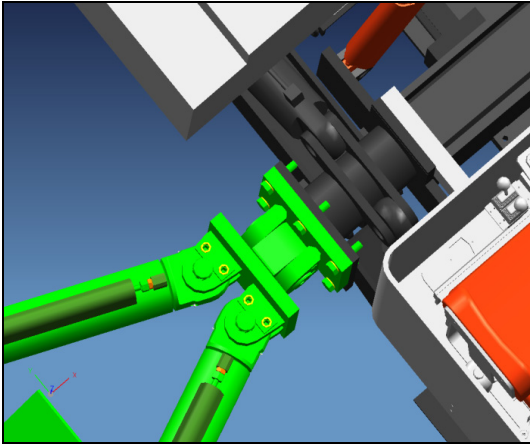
Draufsicht auf die Verschraubung der Vorschubzylinder an der TSM [15]
